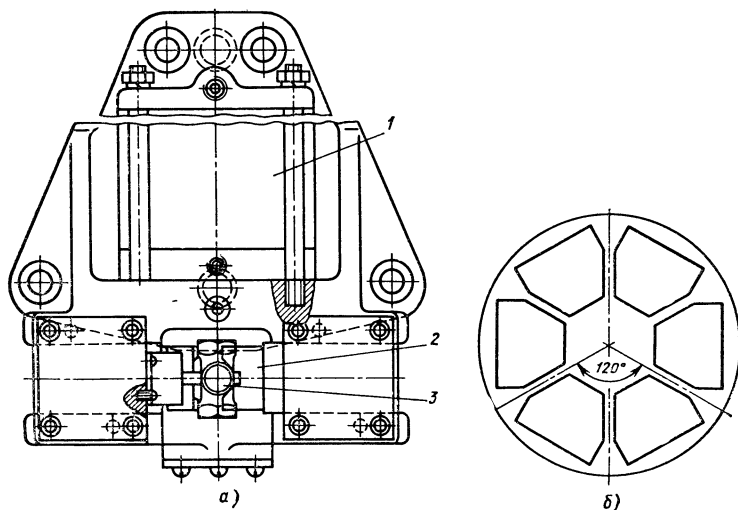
Типовое многопозиционное приспособление, скомпонованное из автономных блоков: а — автономный блок приспособления; б — схема установки блоков на поворотном делительном столе; 1 — пневмоцилиндр; 2 — самоцентрирующие тиски; 3 — обрабатываемая деталь
